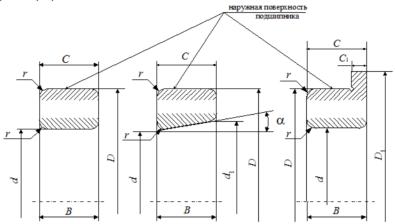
Обозначения основных размеров радиальных и радиально-упорных подшипников.
